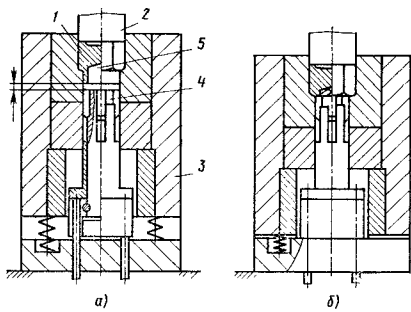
Схема инструмента для образования шлицев в корончатой гайке
